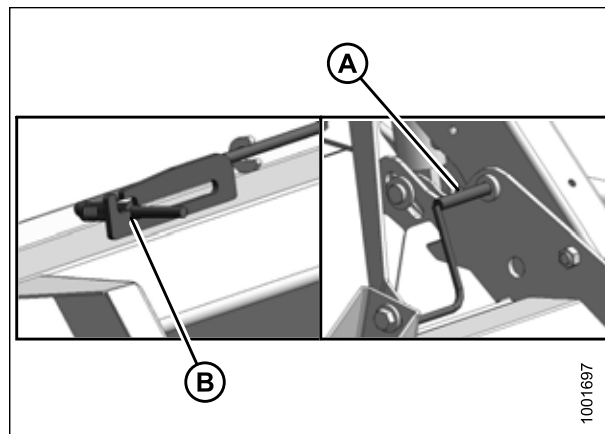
Предохранительный упор подбирающего мотовила — центральный рычаг
